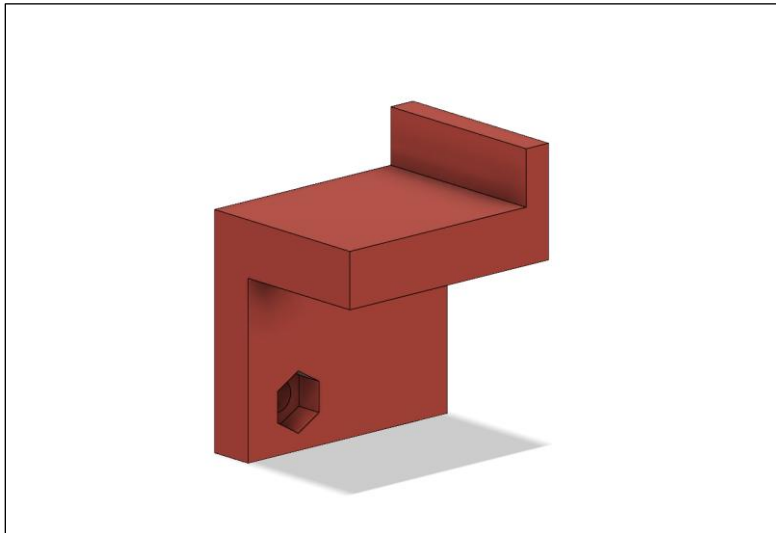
3D Ansicht Auflage Elektronikplatte
